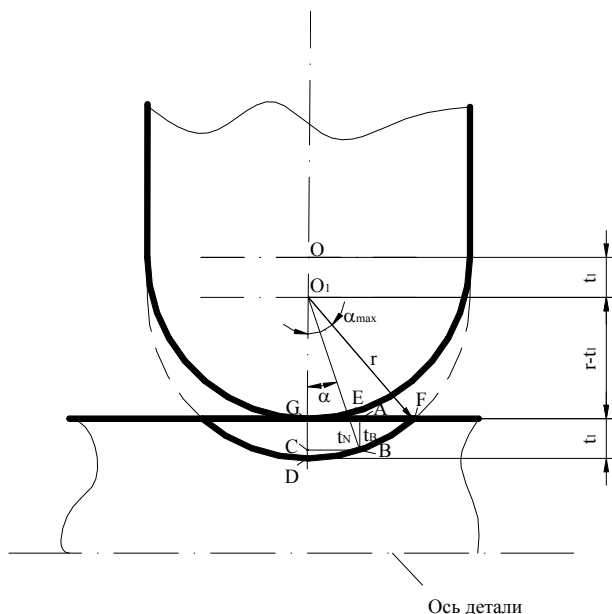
Схема формирования канавки резьбы полукруглого профиля для первого прохода.
